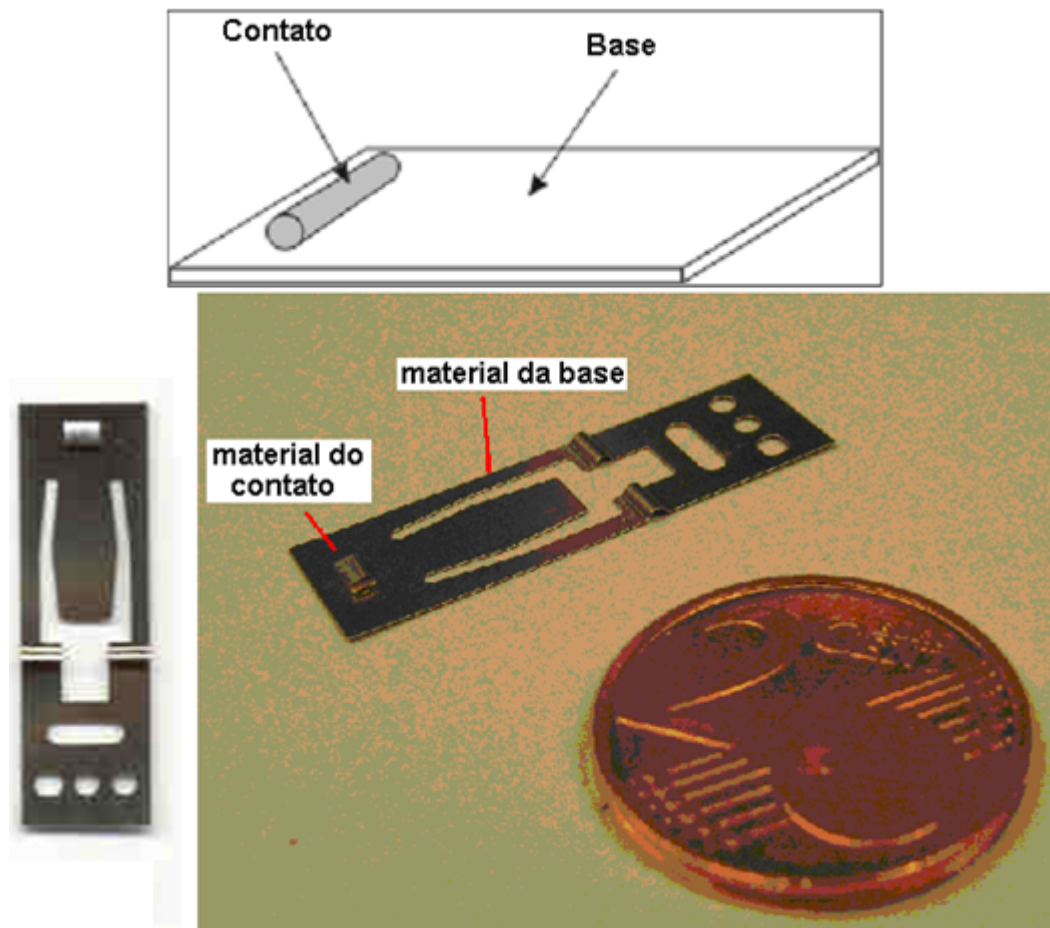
Esquemático das partes a serem soldadas (superior) e contato elétrico após soldagem (inferior)
